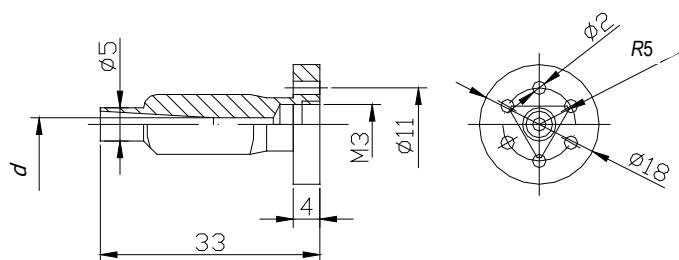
Габаритные и присоединительные размеры паровых сопел
